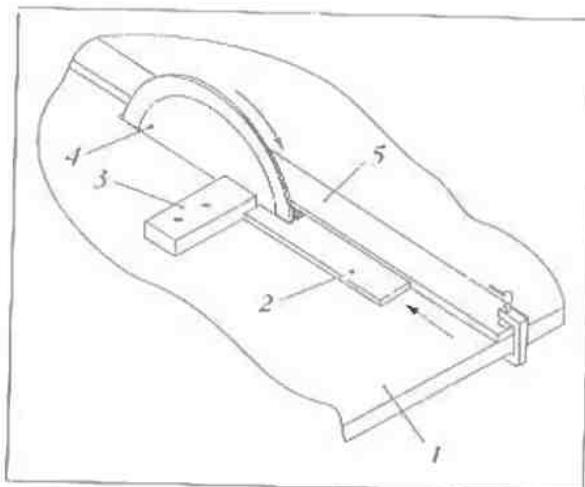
Нарезание зубьев гребня на циркулярной пиле: 1 – рабочий стол; 2 – зажимка; 3 – упор; 4 – фреза; 5 – направляющая линейка
